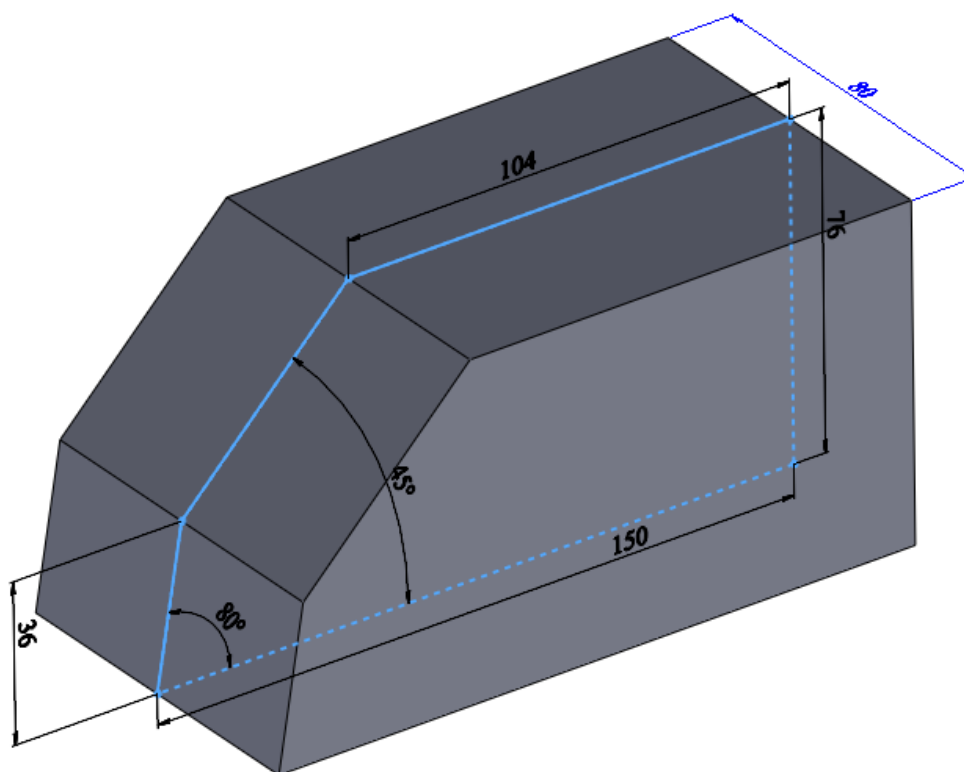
Трехмерная твердотельная заготовка для разработки корпуса ЭС из листового металла
